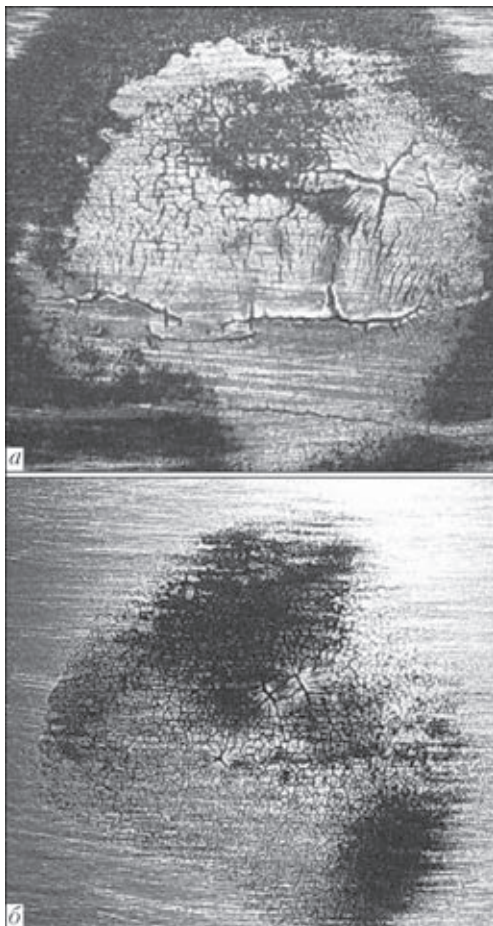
Внешний вид поверхности образцов, наплавленных порошковой проволокой ПП-Нп-35В9Х3ГСФ без подслоя (а) и с подслоем, наплавленным проволокой Св-08А (б), после испытания на термическую стойкость
